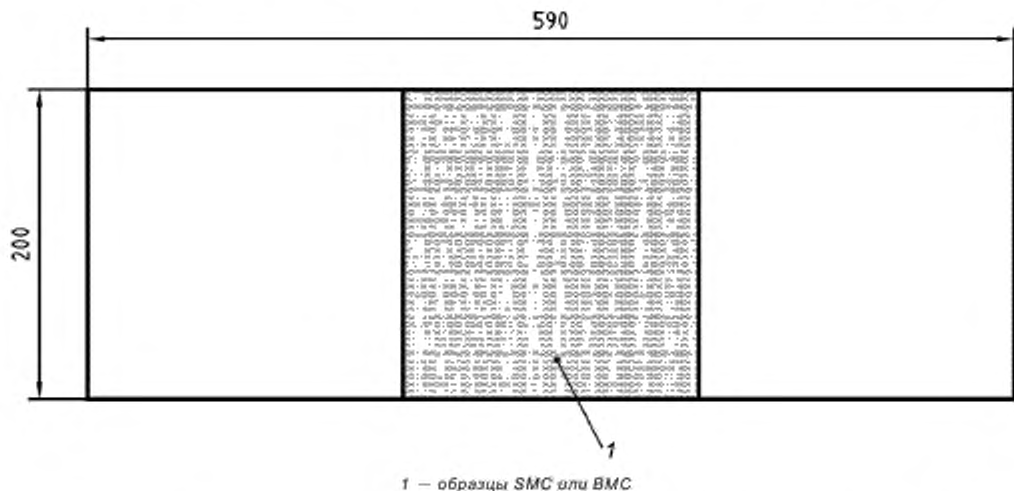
Схема размещения образца в форме при изготовлении пластин по методу В
